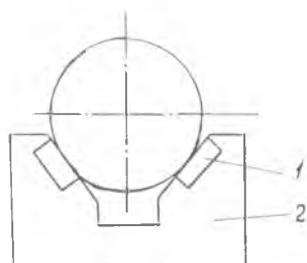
Установка детали в призму с пластинками из твердого сплава
